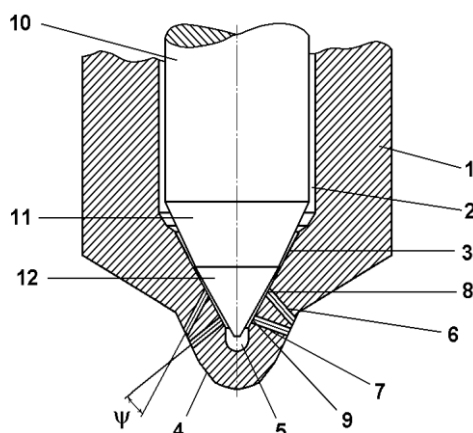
Конструктивная схема распылителя: 1 – корпус; 2 – цилиндрическая полость; 3 – коническая запорная поверхность; 4 – носок распылителя; 5 – подыгольная полость; 6, 7 – распыливающие отверстия; 8, 9 – их входные кромки; 10 – игла; 11 – ее коническая поверхность; 12 – ее запорная часть
